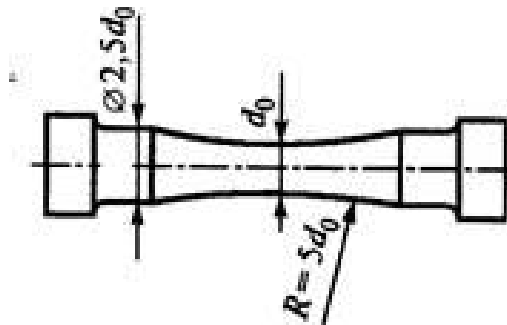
Образец из хрупкого материала для испытаний на растяжение
